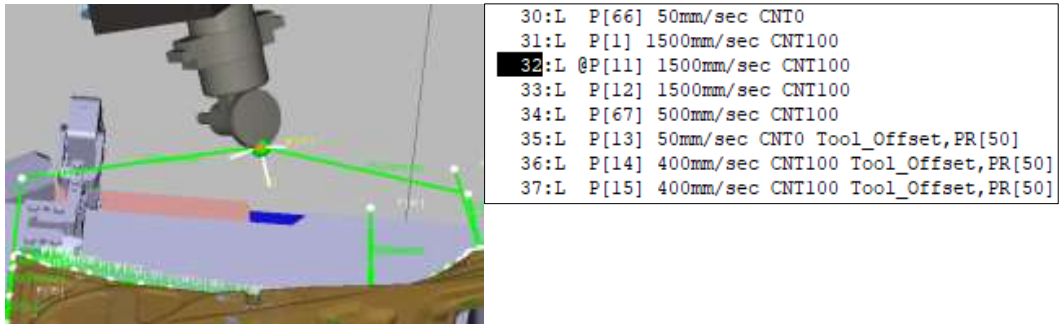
Robot C se mueve a la esquina sin cambiar la roldana.
